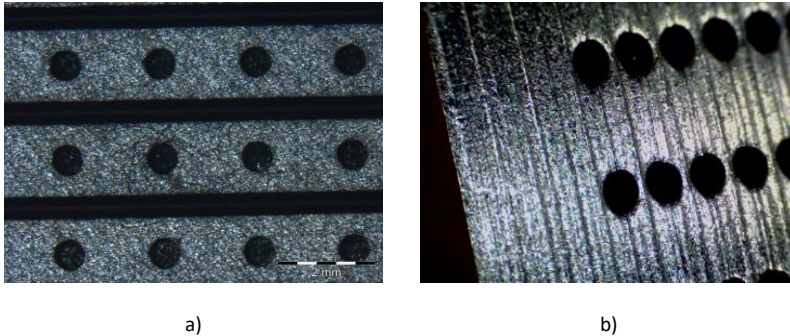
Mikroskopische Aufnahme einzelner Folien der Brennerplatte. a) Lochmuster und Kühlkanäle (Längenmaßstab = 2 mm), b) Seitenansicht der diffusionsgeschweißten Brennerplatte.
